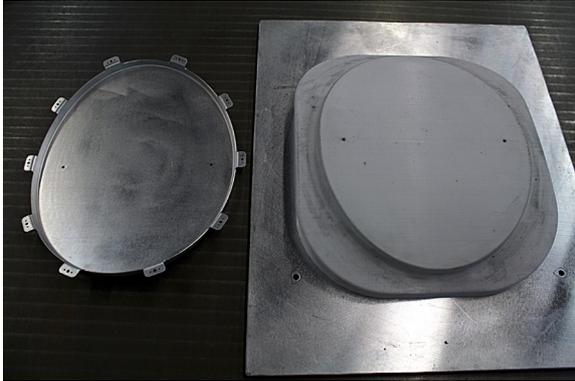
Hydrogeformte Teile bei Piper Aircraft. Das Werkzeug dafür wurde mit der FDM-Technologie gedruckt.
